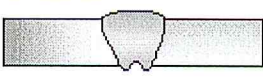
Cordon de soudure présentant des inclusion métallique
